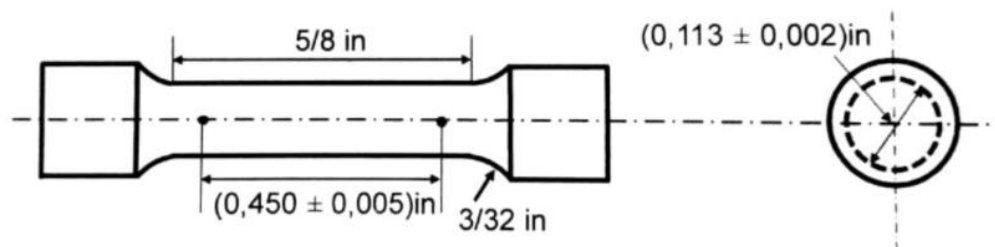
Dimensiones principales de probetas ASTM E-8 utilizadas; Montilla et al (2017)
